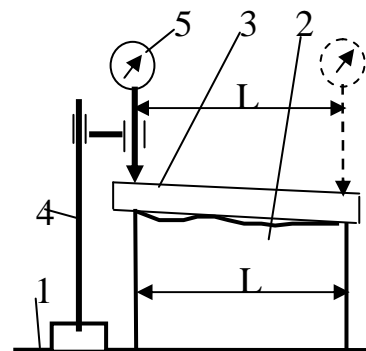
Схема для визначення відхилення від паралельності: 1 – поверочная плита; 2 – деталь; 3 – поверочная линейка; 4 – штатив; 5 – измерительная головка
